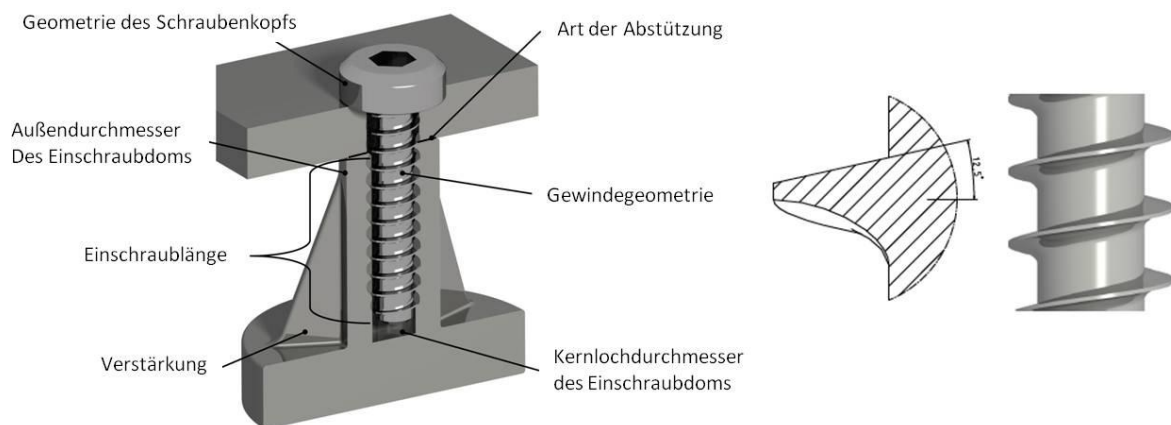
Aufbau einer gewindeformenden Direktverschraubung [26]
